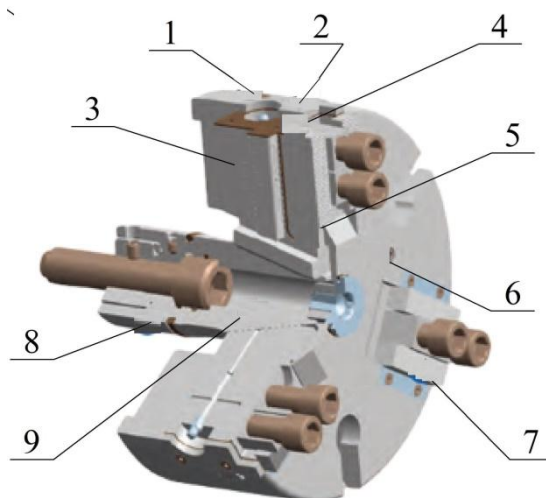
Конструкция современного типового трехкулачкового патрона для токарного станка с ЧПУ: 1 – корпус; 2 – запирающая крышка; 3 – базовый кулачок; 4 – плоское уплотнение; 5 – прямоугольное уплотнение; 6 – крышка; 7 – скребковые планки; 8 – О-образное кольцо; 9 – поршень
